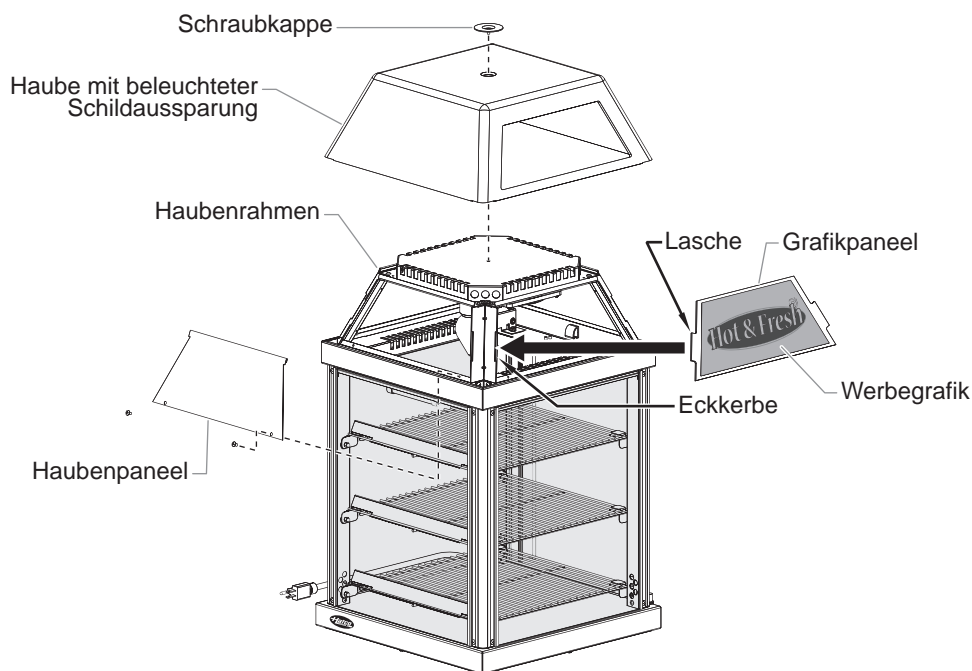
Haube mit von hinten beleuchteter Schildaussparung
